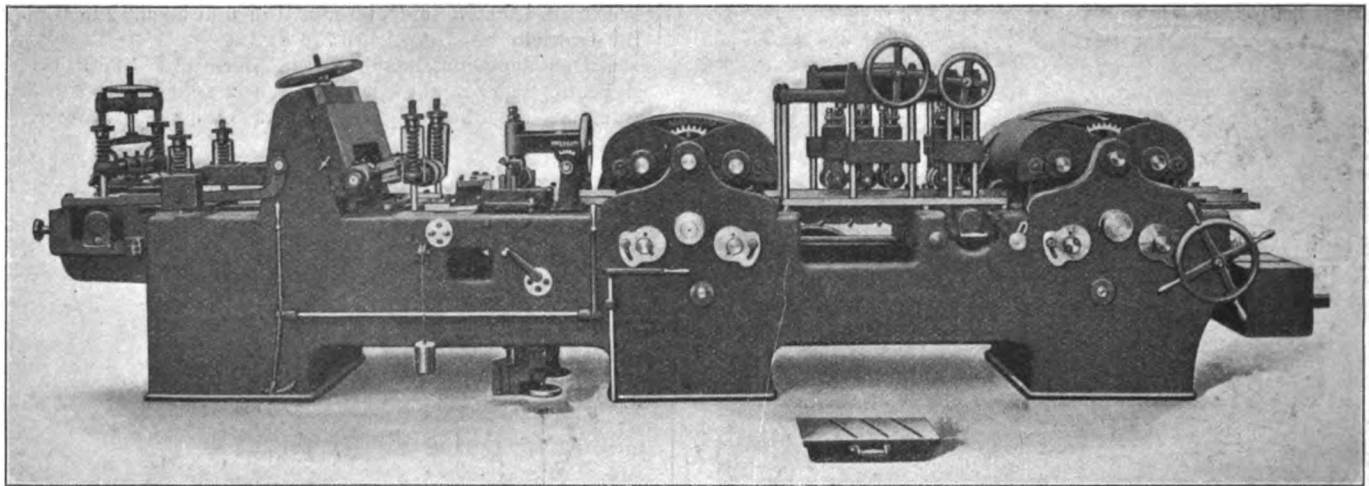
Holzhobelmaschine für Fußbodenbretter, gebaut von der Beronius Mekaniska Verkstad A.-B.
